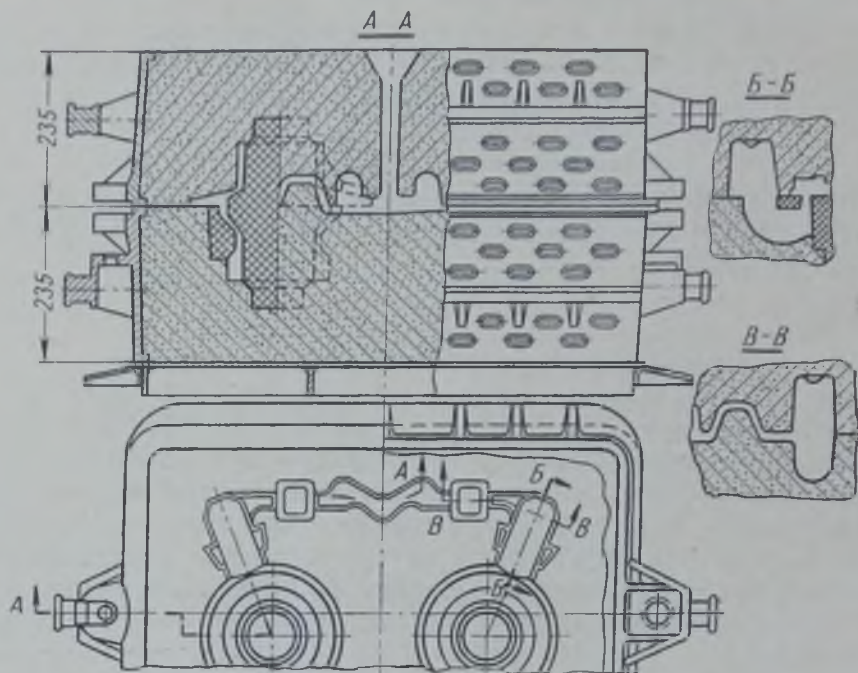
Форма для отливки ступицы заднего колеса автомашины
